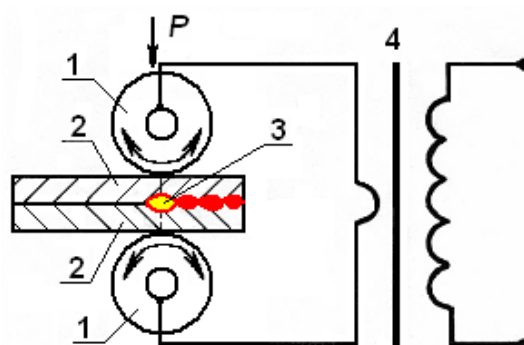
6. Схема шовной (роликовой) электроконтактной сварки
